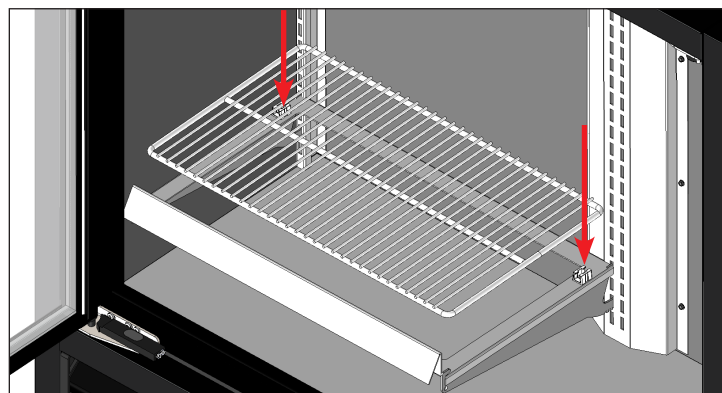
Zamontowany uchwyt wspornikowy półki.
